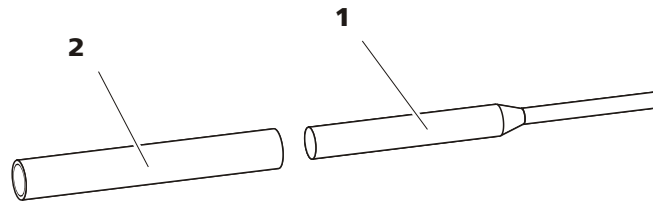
Werkzeug für Kolbendichtung 6.2617.010
